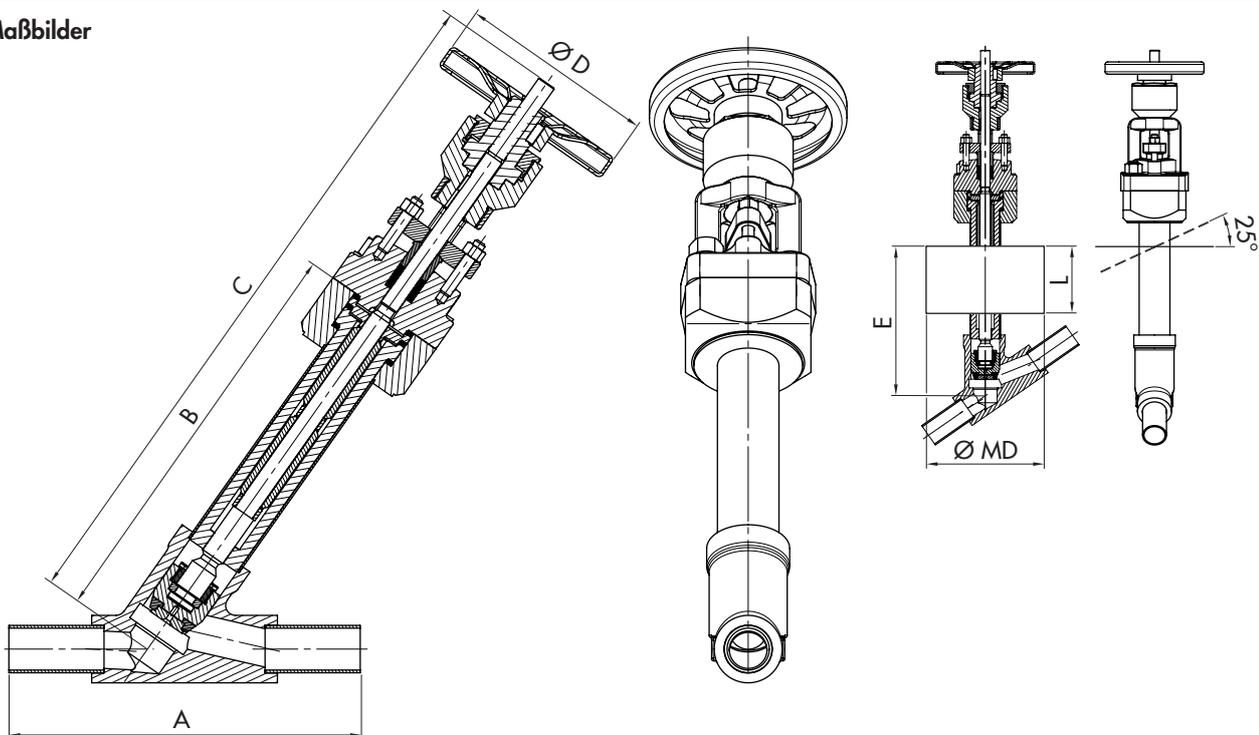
Schrägsitzventil Typ 3588 mit Y-förmigem Strömungsverlauf · Darstellung rechts: Kryoausführung
